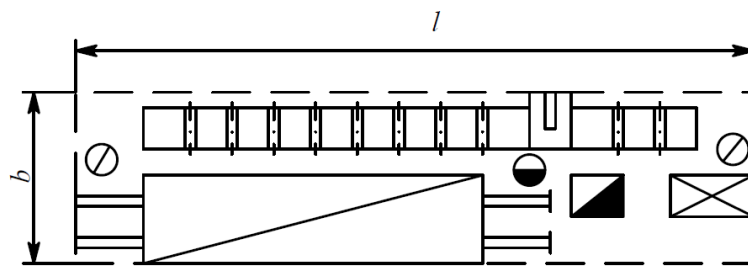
Рабочее место станка ЦМЭ-3А
